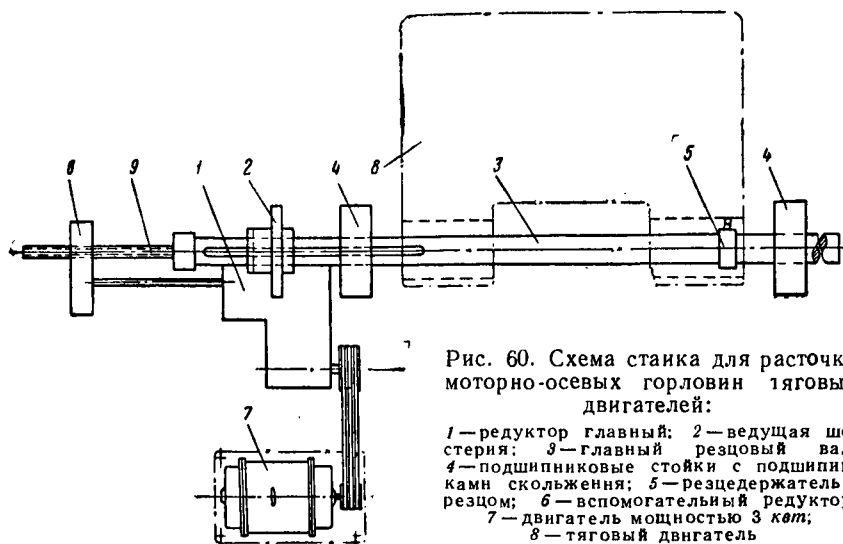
Схема станка для расточки моторно-осевых горловин тяговых двигателей:
